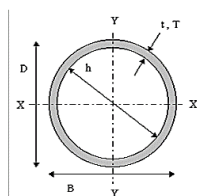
Dimensiones esquemáticas aluminio 22 mm [38].
